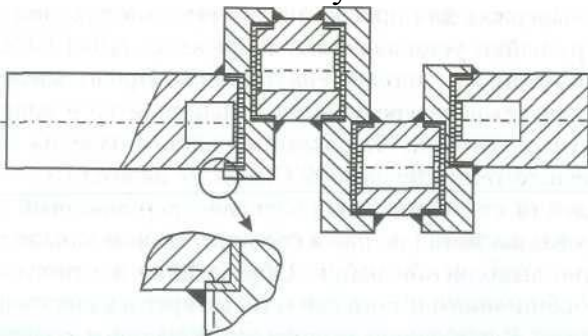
Схема паяного колінчастого вала з порожнистими шийками
